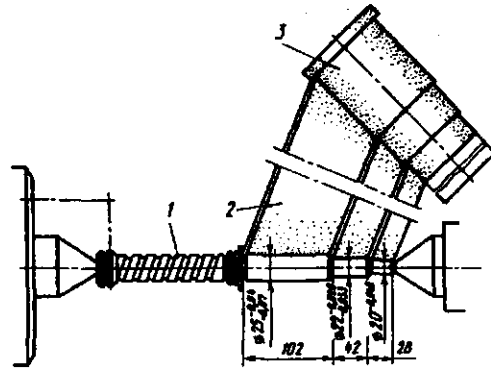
Схема совмещенного шлифования трех шеек, прилегающих фасок и торца на винте гидроусилителя руля автомобиля ЗИЛ-130: 1 – обрабатываемая деталь; 2 – шлифовальные круги; 3 – алмазный правящий ролик
